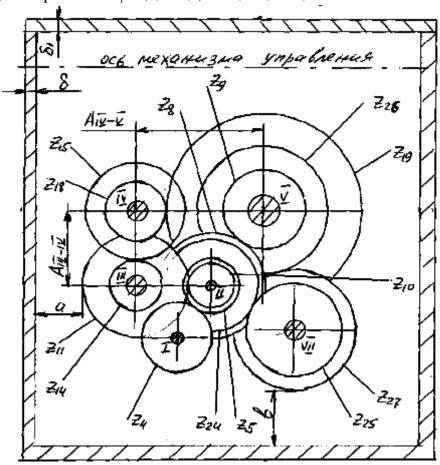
Эскизная компоновка свертки коробки скоростей.
